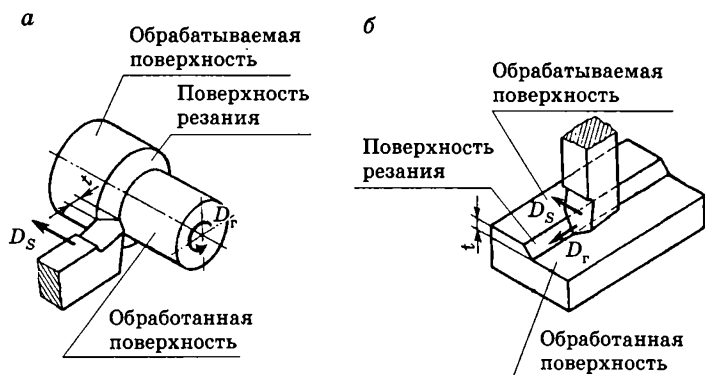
Поверхности на обрабатываемых заготовках:
